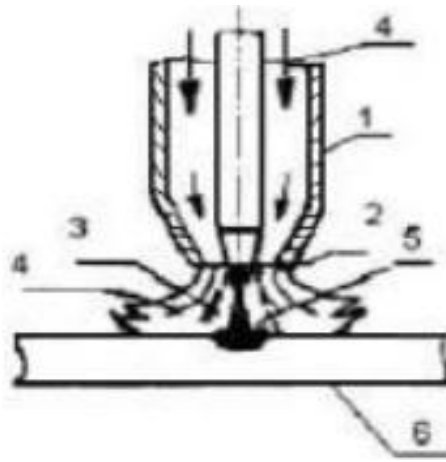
Схема подачі захисного газу до зони зварювання: 1 – сопло; 2 – електрод; 3 – зона дуги; 4 – захисний газ; 5 – розплавлений метал зварювальної ванни; 6 – деталь
